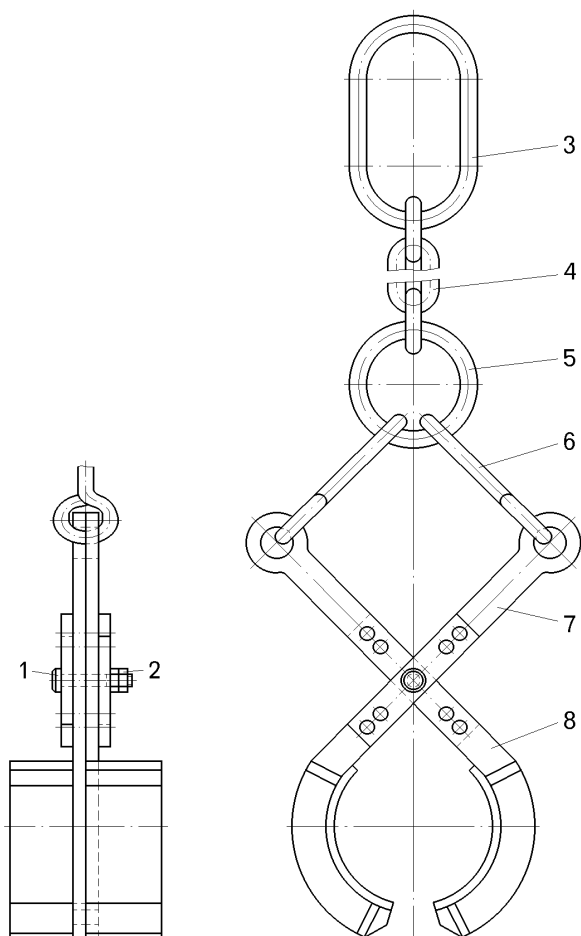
Подвеска для снятия и установки карданного вала:
